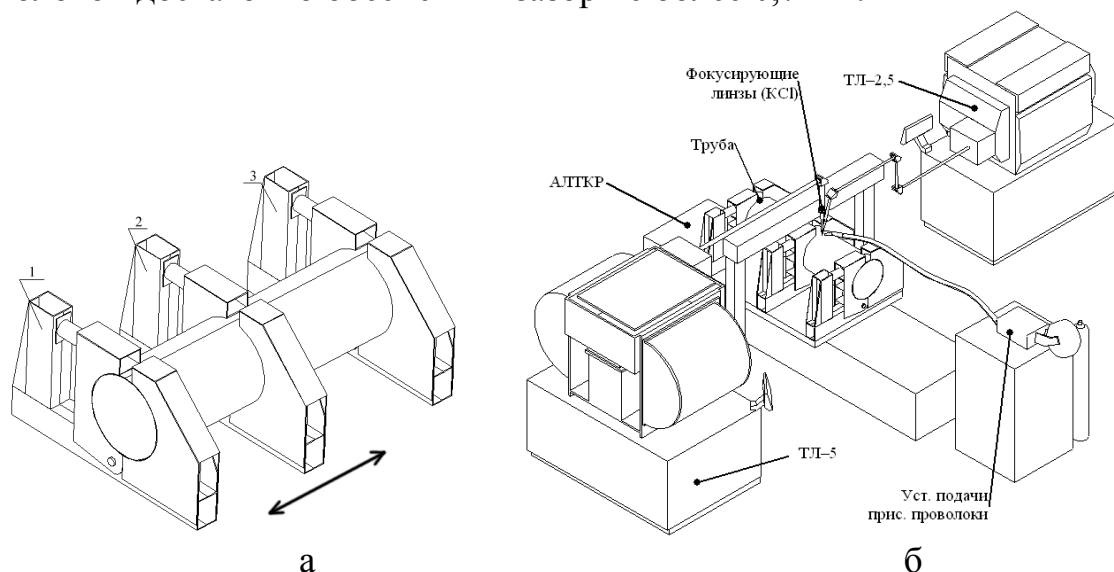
Трёхмерная схема: а) кондуктора для сборки трубной заготовки; б) сварочный стенд с двумя лазерами.
